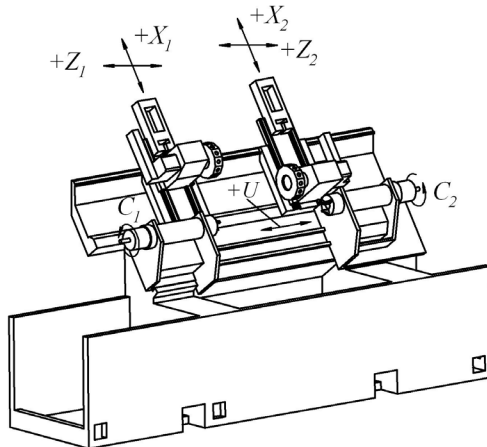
Принципиальная схема токарного обрабатывающего центра с противопинделем
